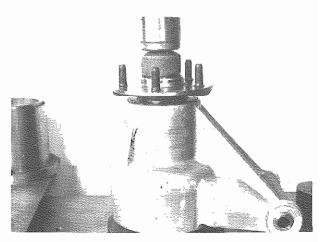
Base portamozzo n. 8 Hub holder face No. 8
